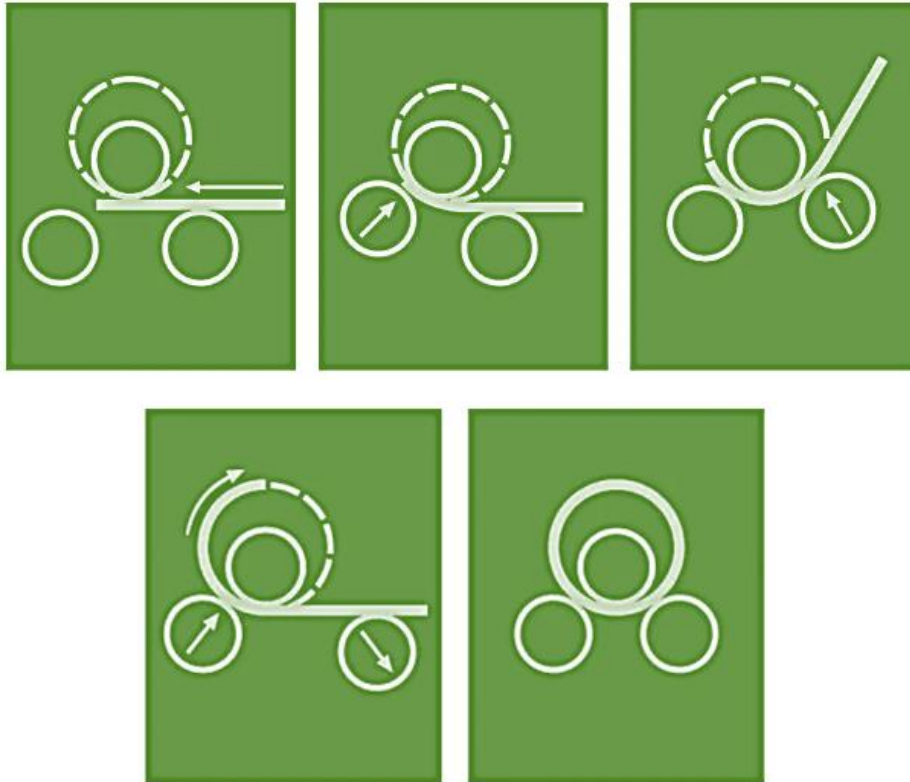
Схема і послідовність вальцювання циліндричної заготовки
